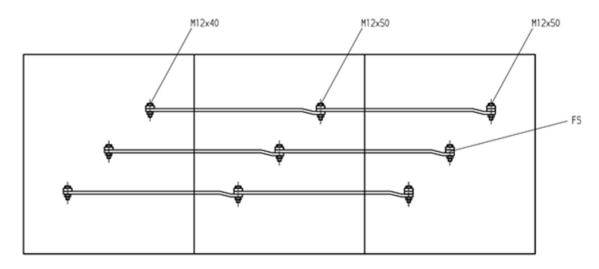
Sammelschienenanschluss Flachleiter Рис. 24-1: подключение сборной шины проводов прямоугольного сечения
